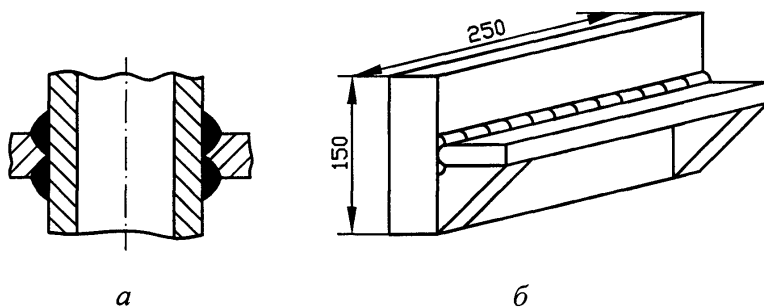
Контрольные сварные соединения для проведения металлографического контроля
